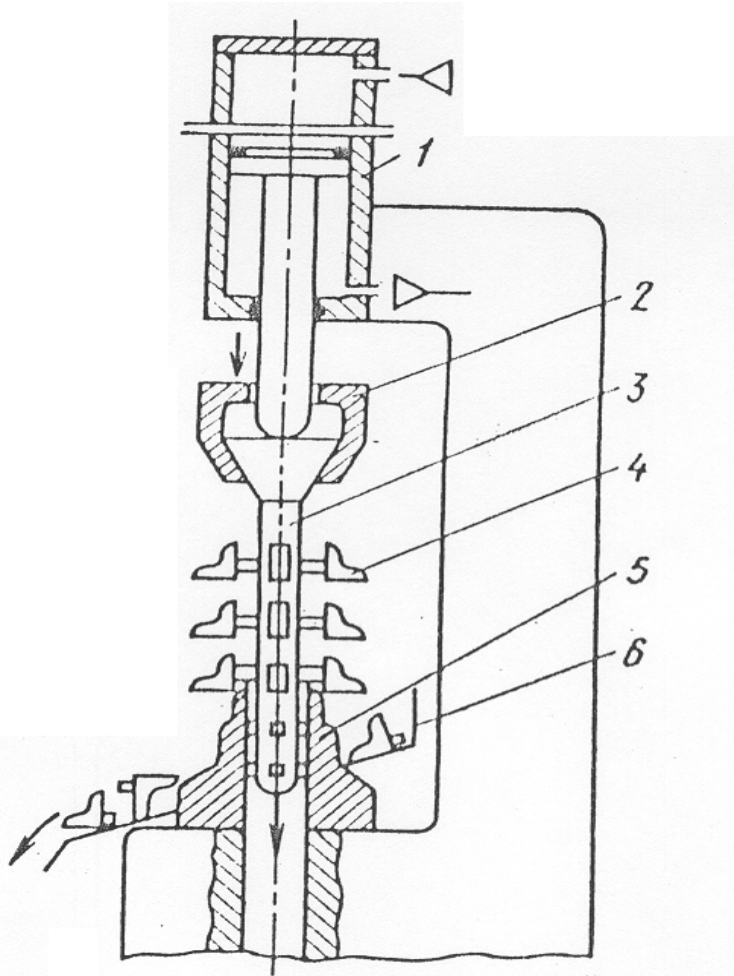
Схема устройства пресса для отделения отливок от стояка: 1 – гидроцилиндр; 2 – зажим; 3 – блок отливок; 4 – отливки; 5 – штамп; 6 – лоток.
